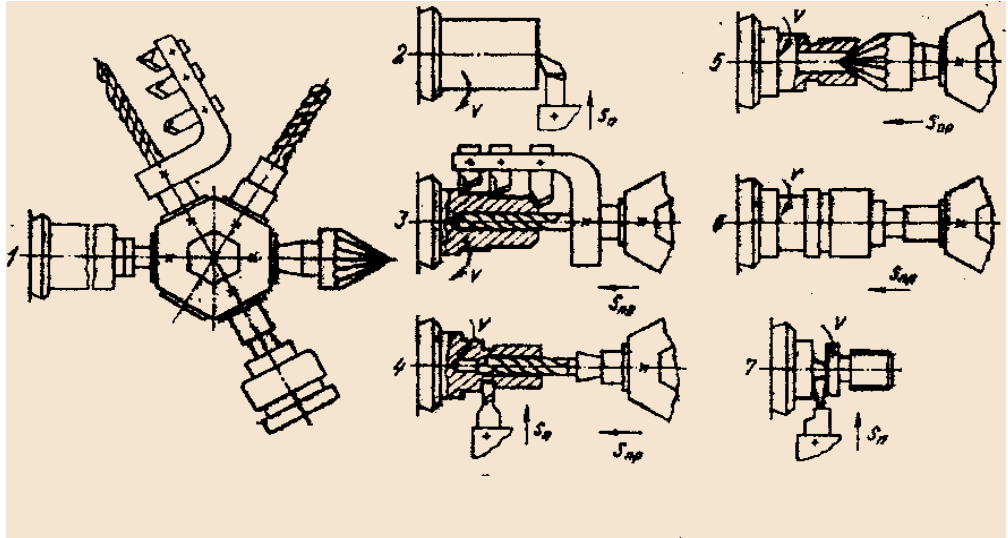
, б – патронный токарно-револьверный полуавтомат 1740РФ3 и схемы обработки поверхностей заготовок:
